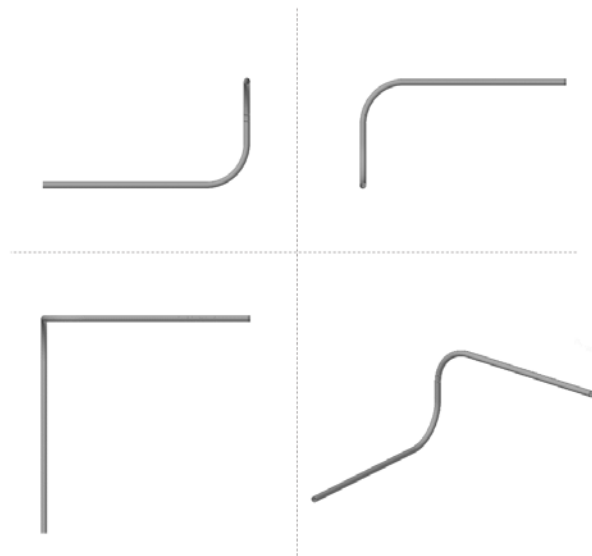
Vistas del tubo de calor. Vista lateral, izquierda arriba. Vista frontal, derecha arriba. Vista superior, izquierda abajo. Perspectiva, derecha abajo.
